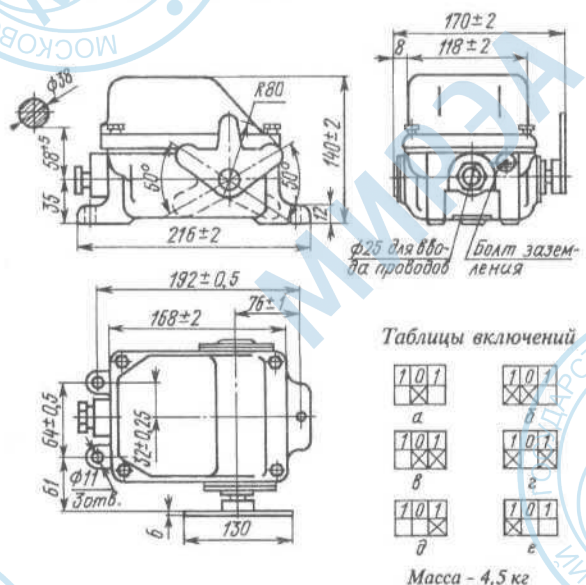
Габаритные, установочные размеры и масса выключателя типа КУ-744
